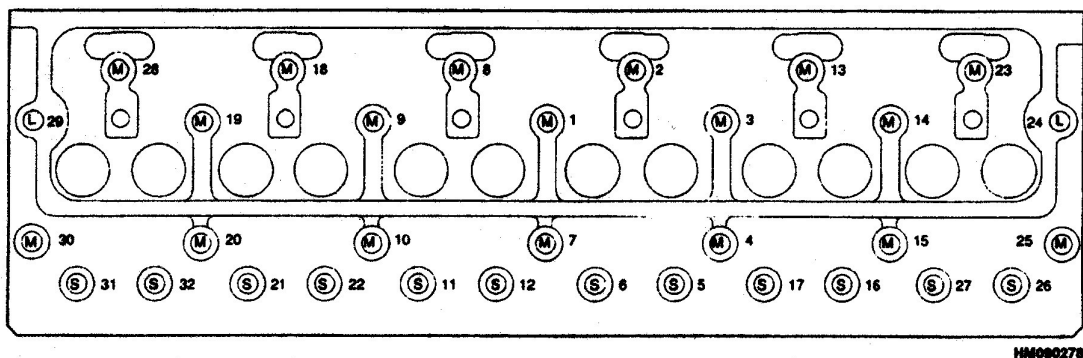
Последовательность подтяжки крышки цилиндра, шестицилиндровые двигатели
